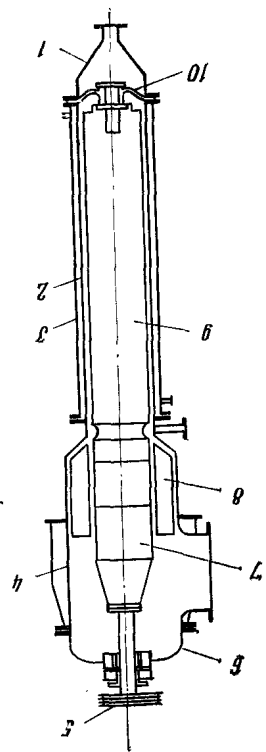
Пленочный испаритель с роторной мешалкой типа «Лува»: 1 — конусное днище; 2 — корпус аппарата; 3 — рубашка для теплоносителя; 4 — сепарационная камера; 5 — приводной шкив мешалки; 6 — крышка аппарата с сальниковым устройством; 7 — роторный каллеуловитель; 8 — распределительное кольцо; 9 — роторная мешалка; 10 — подшипниковый узел
